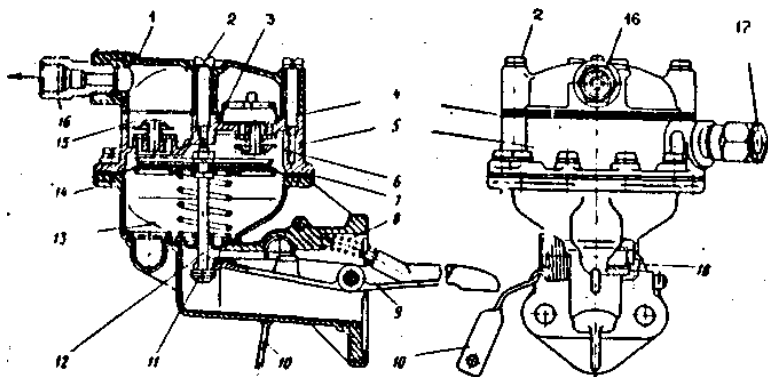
Паливний насос: 1 – кришка; 2 – з'єднувальний гвинт; 3 – сітчастий фільтр; 4 – резинова прокладка; 5 – головка насоса; 6 – впускний клапан; 7 – діафрагма; 8 – зворотна пружина коромисла; 9 – коромисло; 10 – важіль ручної підкачки палива; 11 – упорна шайба; 12 – шток; 13 – пружина діафрагми; 14 – корпус насоса; 15 – випускний клапан; 16 – штуцер для відведення палива; 17 – штуцер для підведення палива; 18 – контрольний отвір
